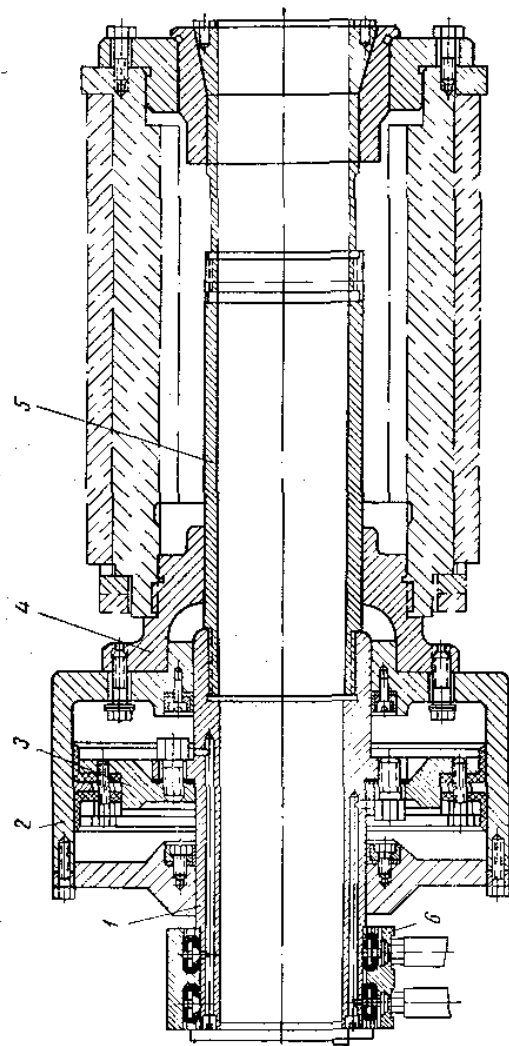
Пневматическое приспособление для зажима длинных заготовок на резьбофрезерном станке
